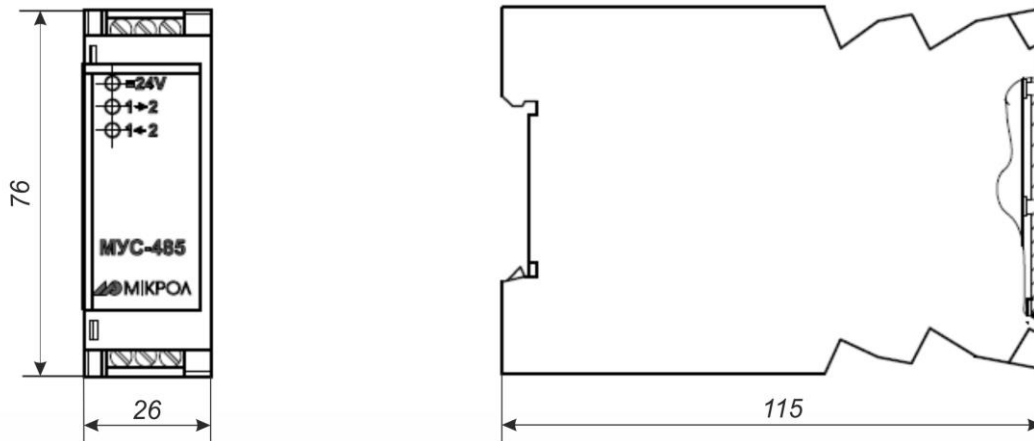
Внешний вид и габаритные размеры блока МУС-485
